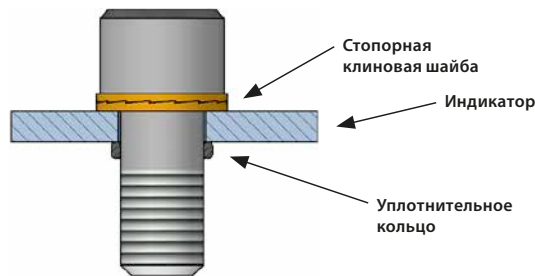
Расположение уплотнительного кольца и шайбы приводного винта
